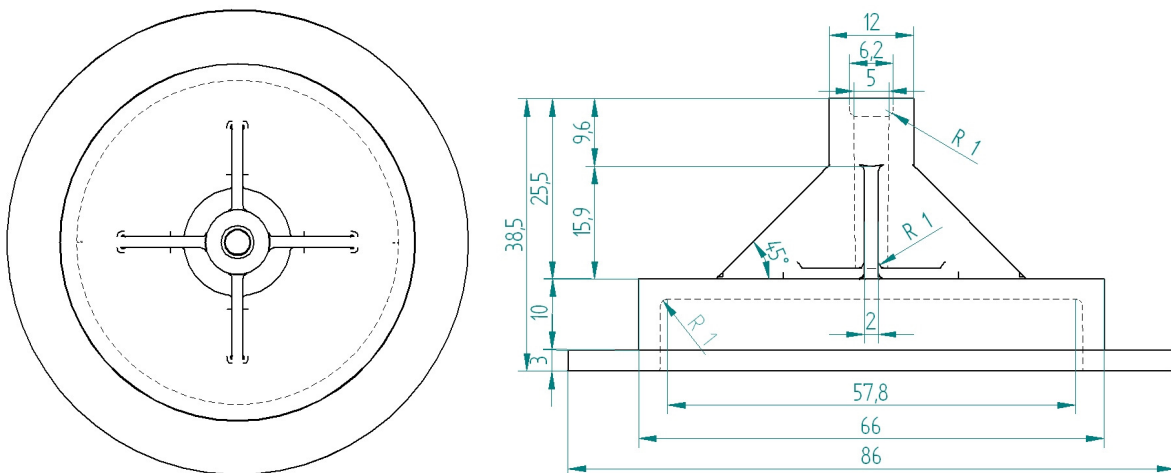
Befestigungsdemonstrator mit 45°-Rippen
